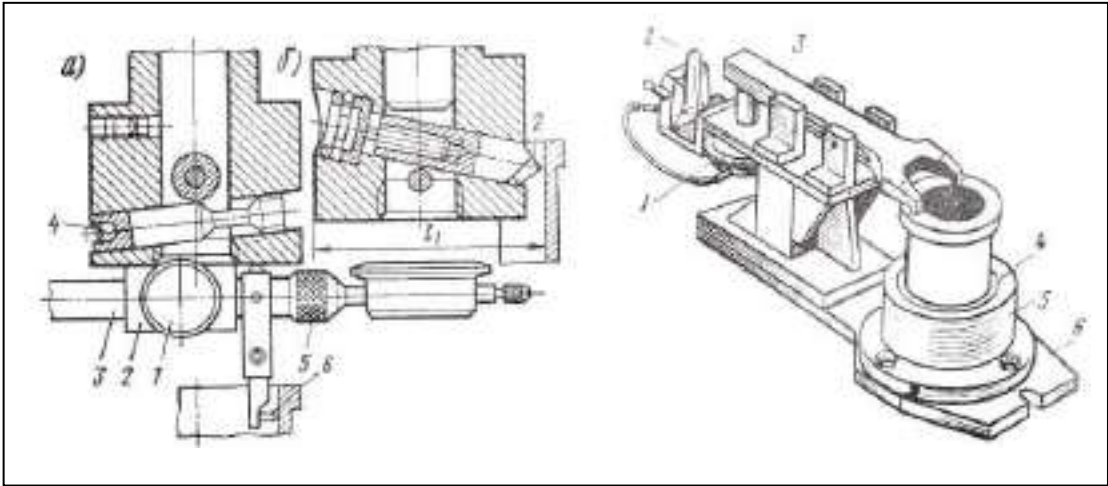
Резцоваяголовка станка2А78НРис.21.Приспособлениедля установкии креп-
